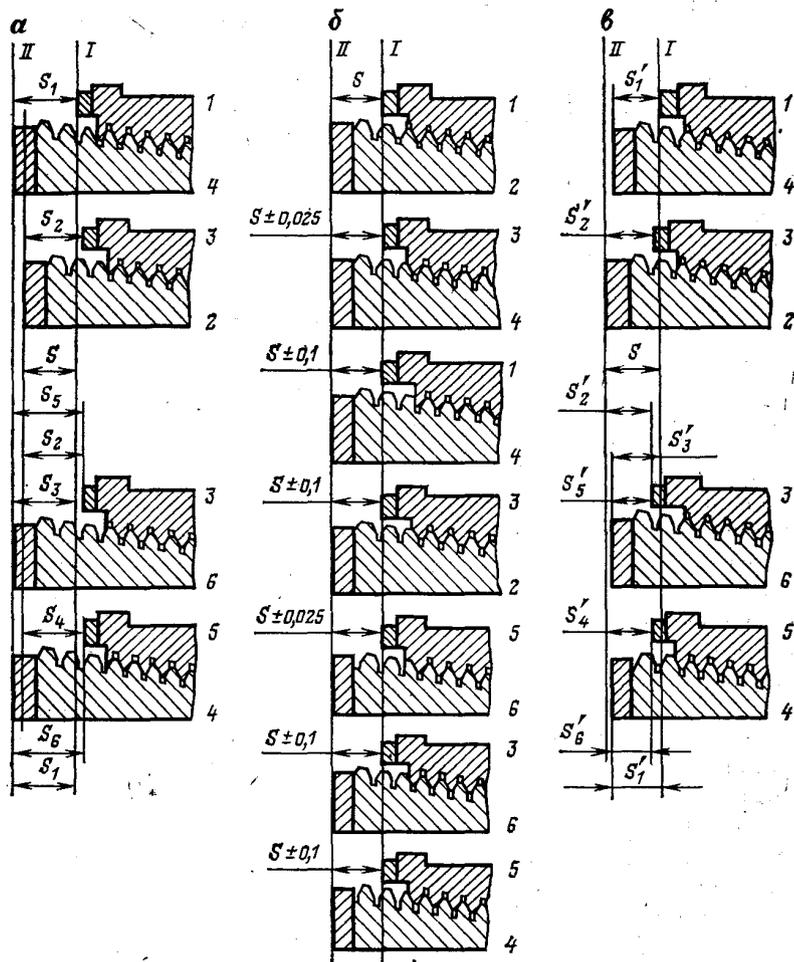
Схема контроля замковой резьбы с помощью образцовых и контрольных калибров:
